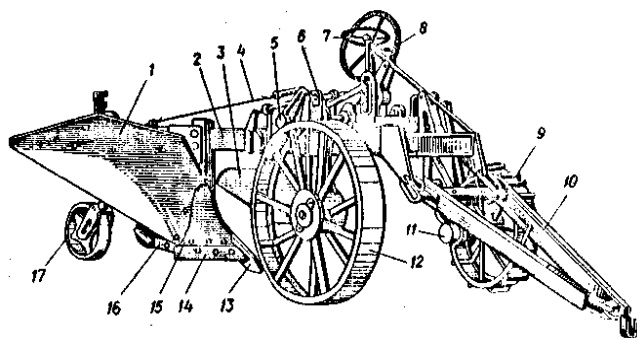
Плантажний плуг ППУ-50А: 1 – корпус; 2 – рама; 3 – передплужник; 4 – тяга; 5 – гідроциліндр; 6 – кулак, 7 і 8 – штурвали; 9 – польове колесо; 12 – борозенне колесо і
